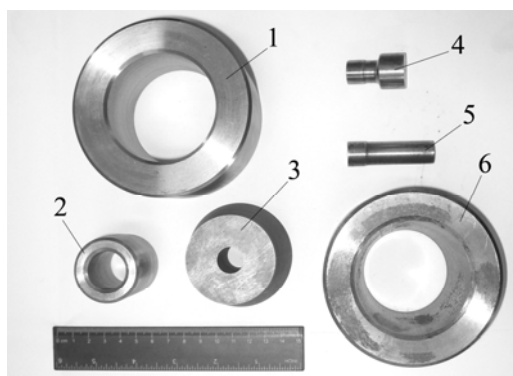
Закрытая пресс-форма для прессования цилиндрических образцов по односторонней схеме нагружения:
